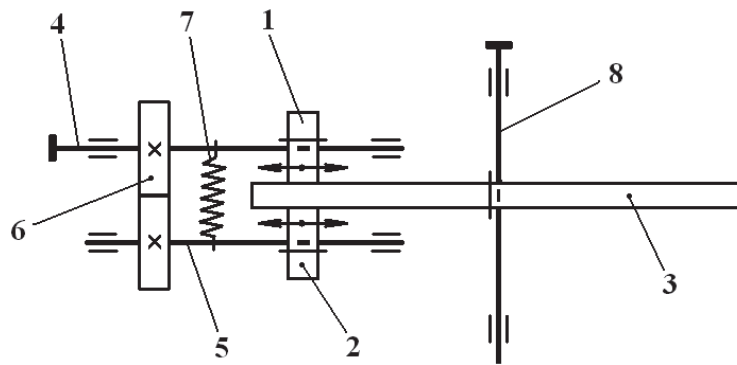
Кінематична схема двопоточного лобового фрикційного варіатора:
